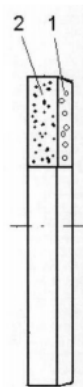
Загальний вигляд пристрою для глибокого шліфування циліндричних поверхонь
